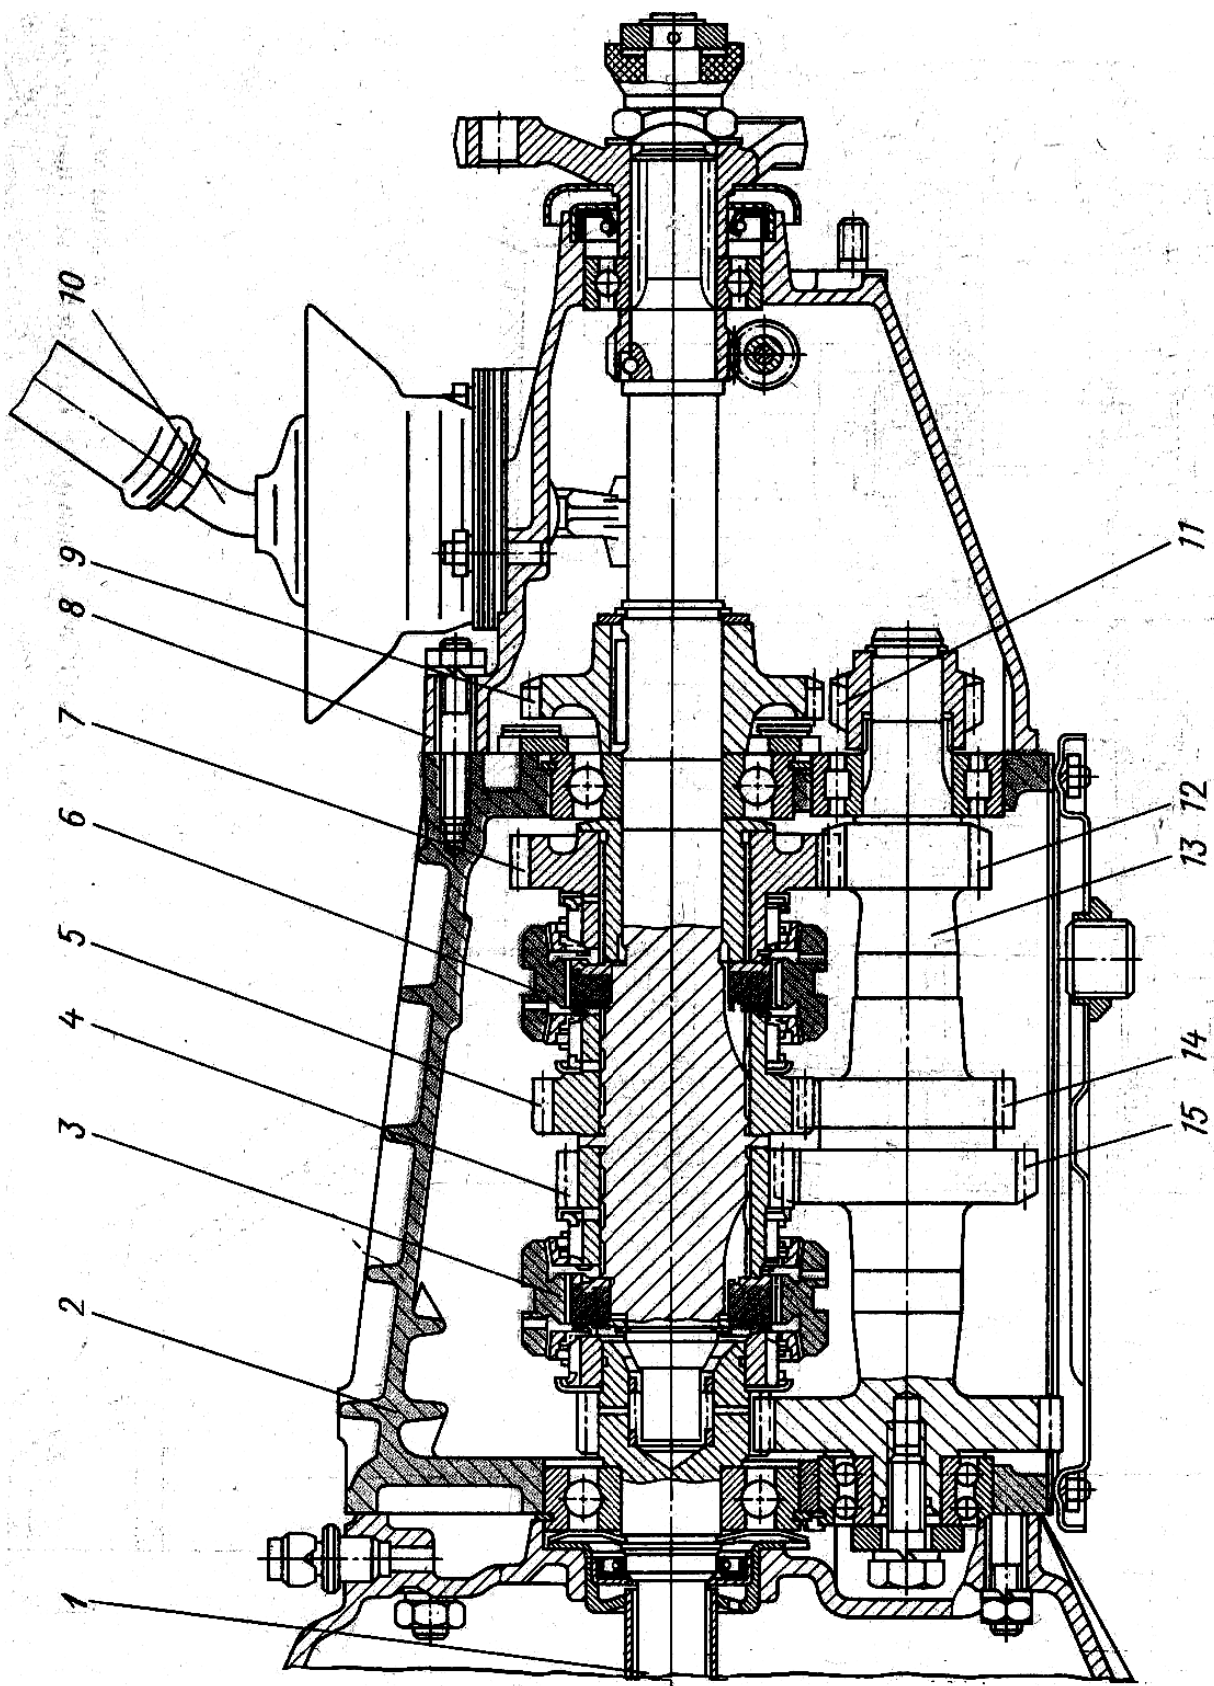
Коробка передач автомобиля ВАЗ-2101
